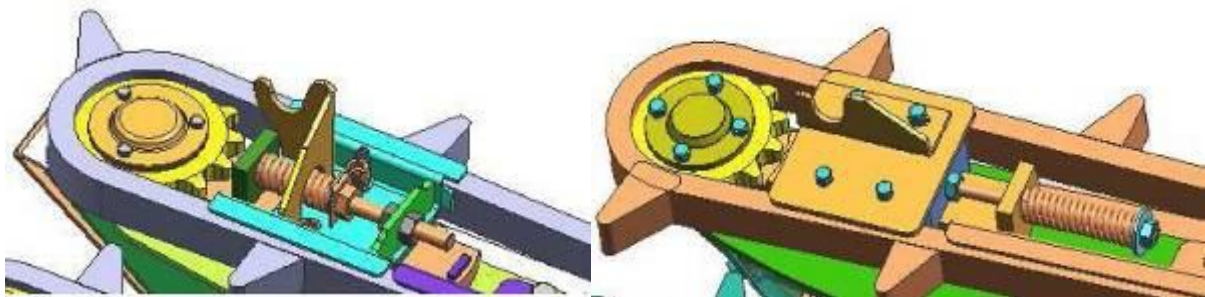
Натяжное устройство серийного приспособления (слева)
